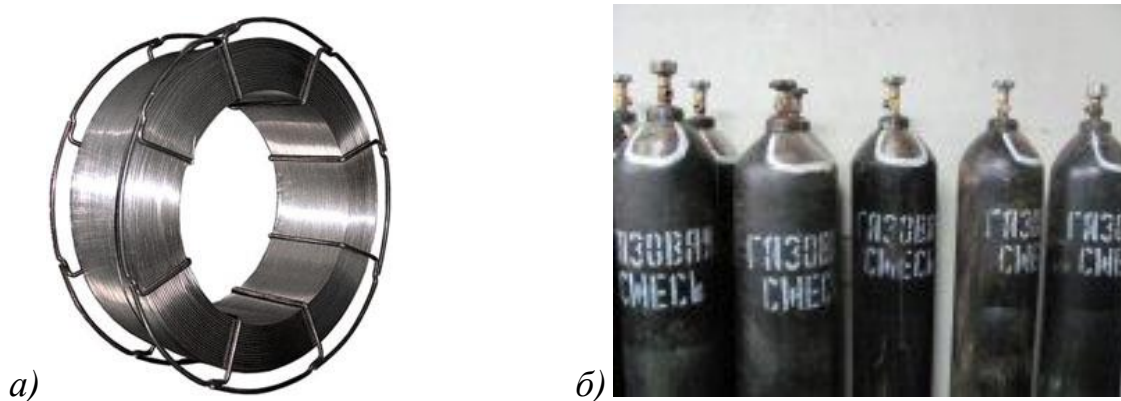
Сварочные материалы: намотанные кассеты с омеднённой сварочной проволокой Св-08ГСМТ (а) и баллоны с защитным газом (б)
